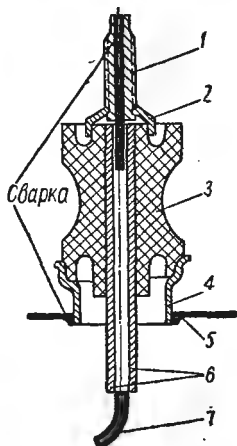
Монтированный изолятор ИКП-8: 1 — шпилька М8; 2 — верхний коваровый колпачок; 3 — изолятор; 4 — нижний коваровый колпачок; 5 — крышка конденсатора; 6 — изоляция токоведущего провода; 7 — токоведущий провод.
